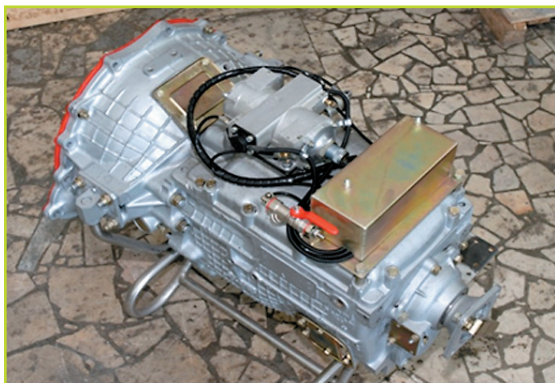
Внешний вид КПП с исполнительным механизмом.
